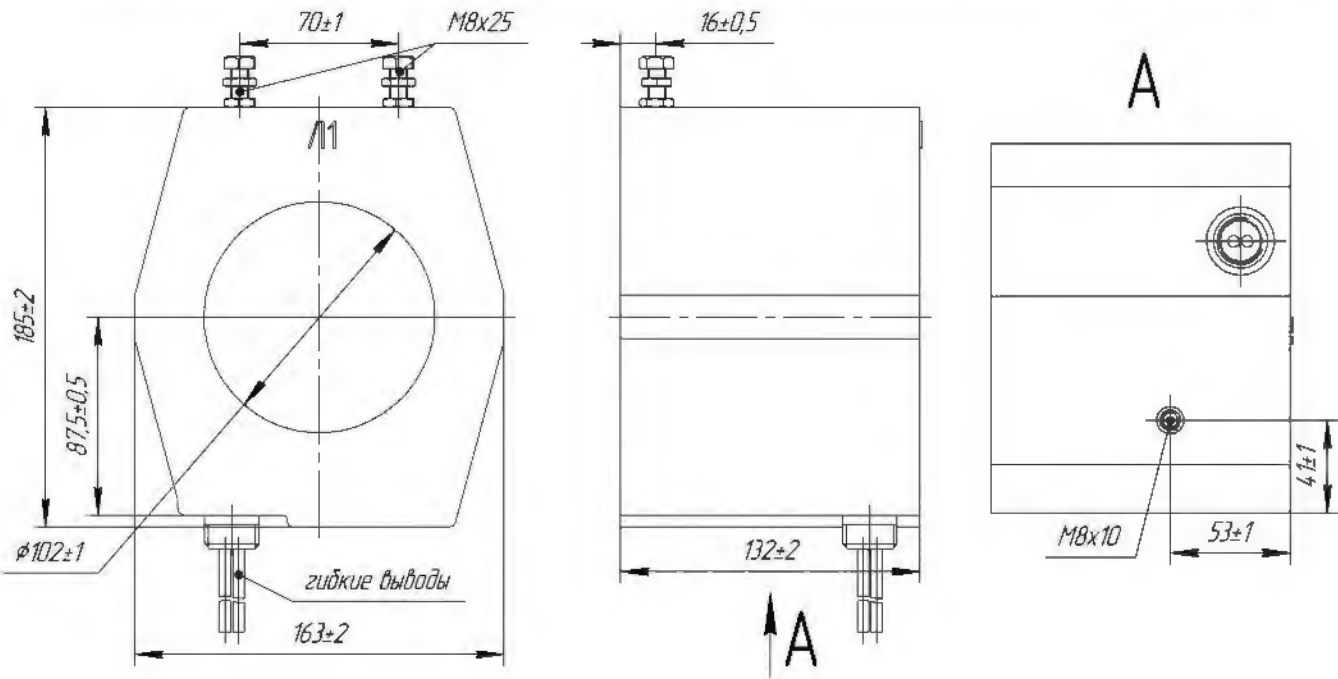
Габаритные и установочные размеры трансформатора тока ТП-ЭК-0,66 М9.
